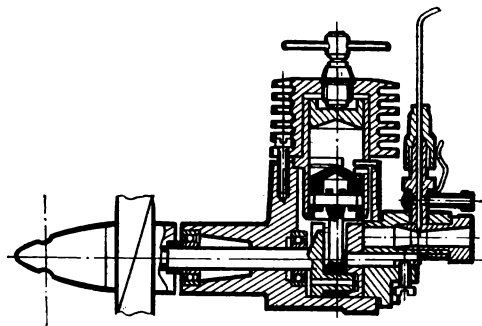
Конструкция двигателя МК-17 «Юниор».
